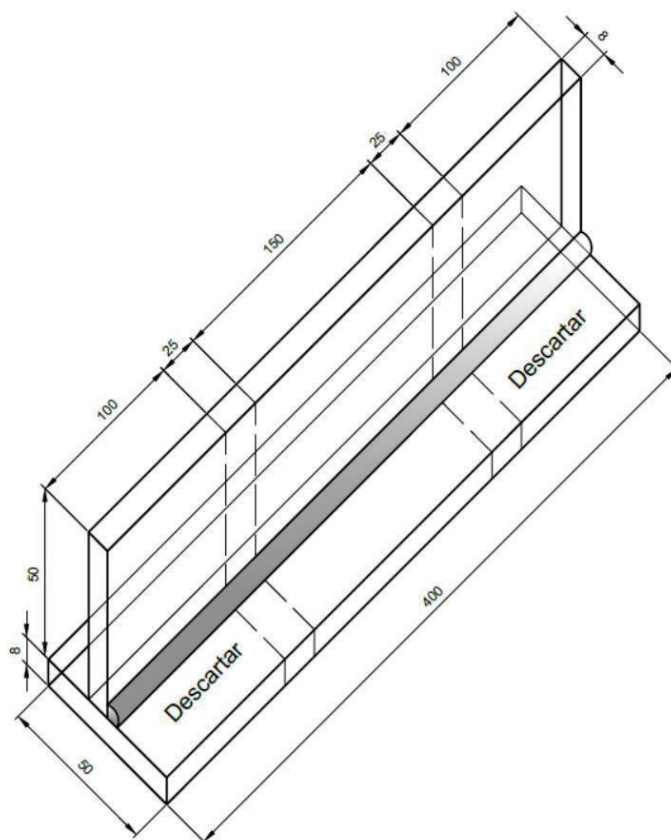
Esquema para realización de corte de las juntas soldadas.
